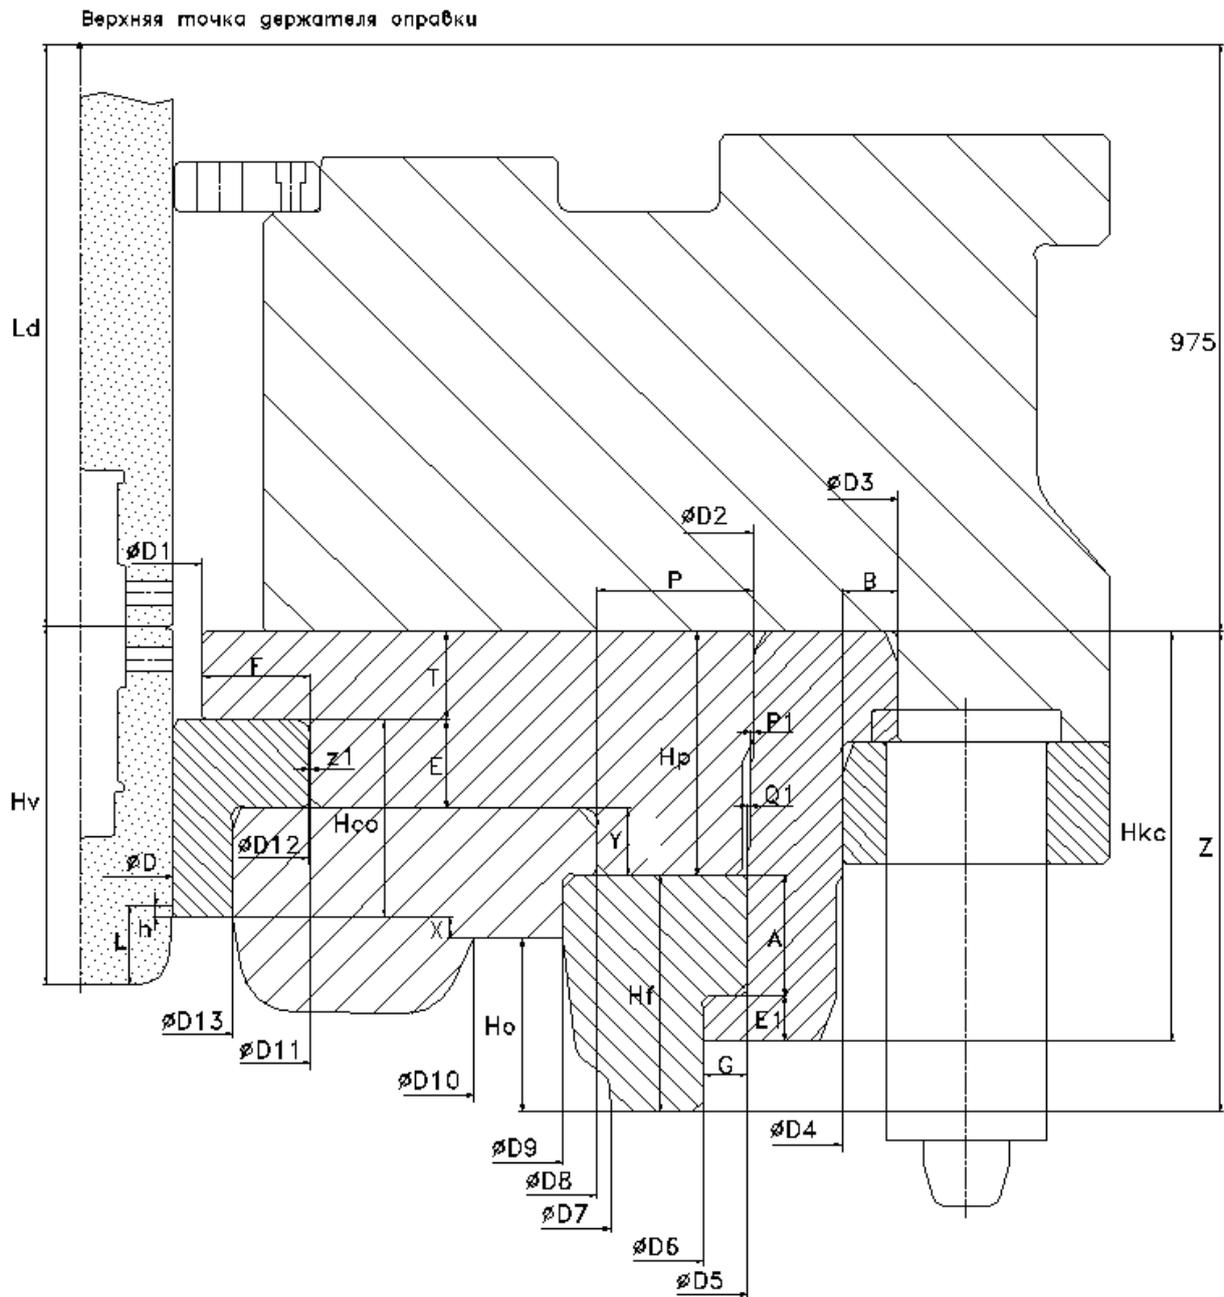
Схема размеров инструмента сборочного чертежа формовочного пресса (верхний штамп)
